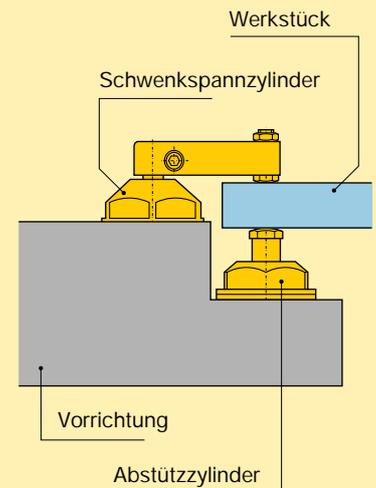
Der Einsatz einer Kombination aus Schwenkspannzylinder und Abstützzyylinder.
